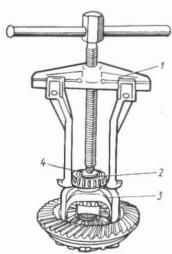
Desmontaje del aro interior del cojinete de la caja del diferencial con el extractor universal A.40005/1/6:
